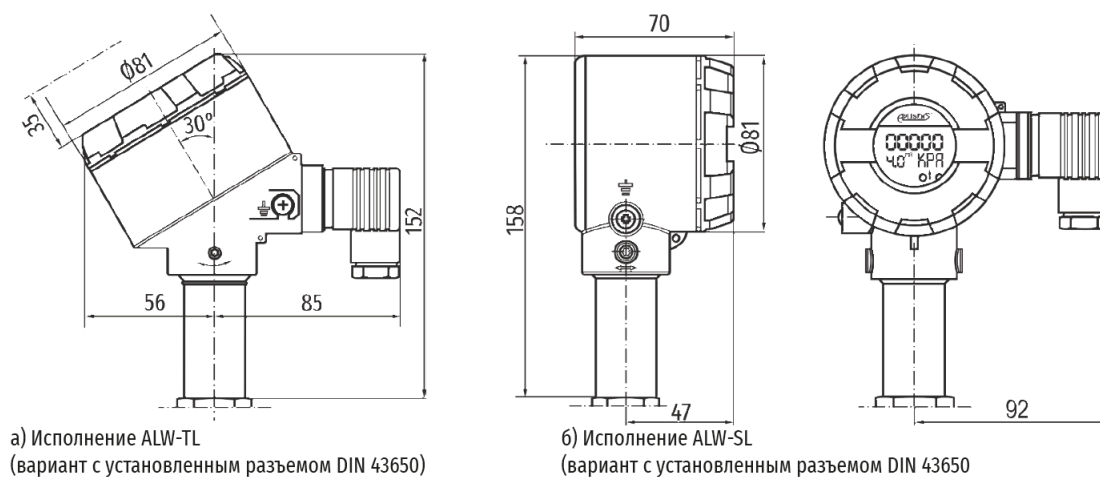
Исполнения корпусов с индикатором ALW-TL и ALW-SL, габаритные размеры
